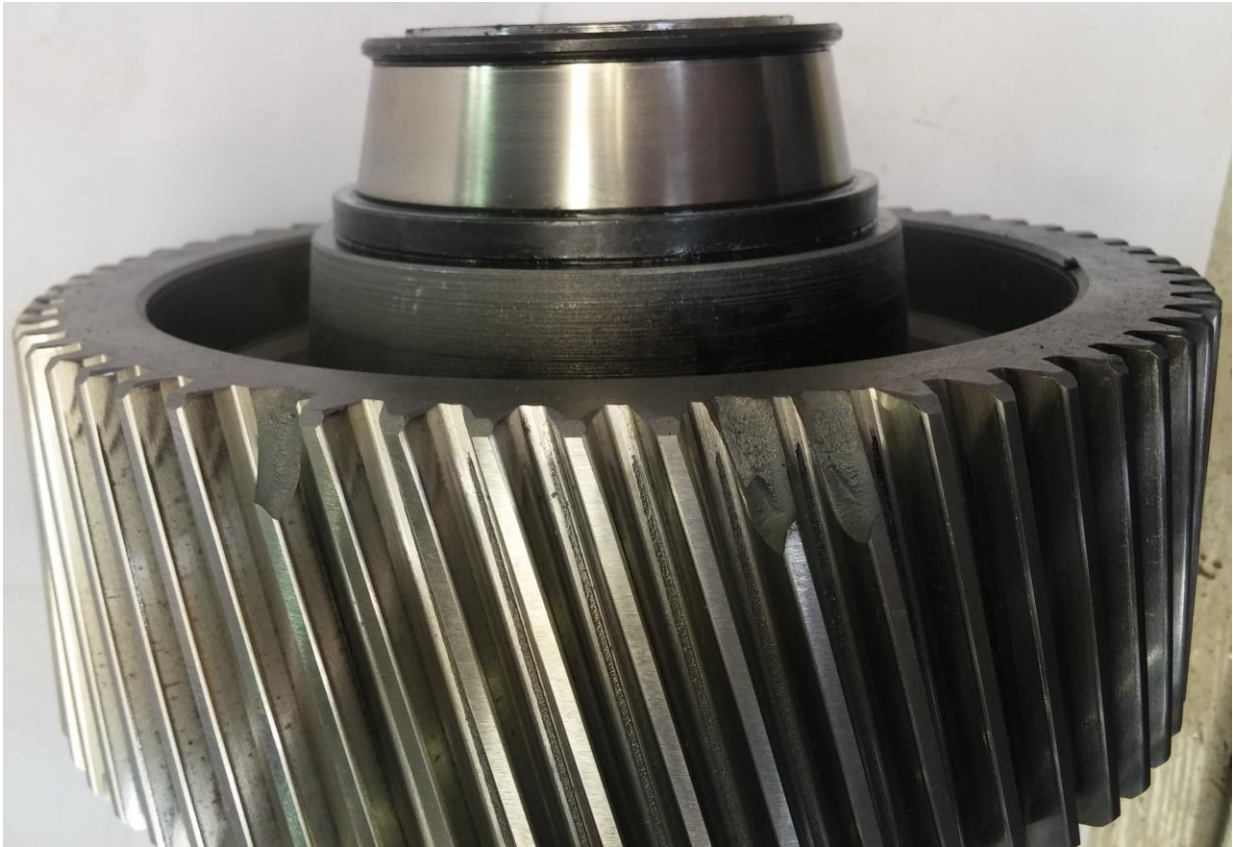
Внешний вид выходного колеса редуктора с эвольвентным зубчатым зацеплением после испытаний
